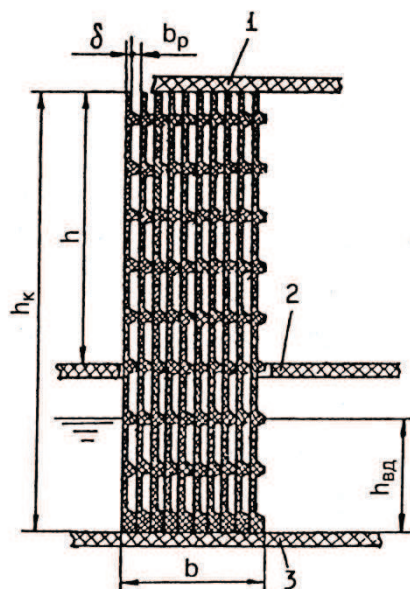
Принципиальная схема устройства и компоновки орошаемой ламинарной насадки из пластин мипласта для воздухоохладителя: 1 – крышка корпуса; 2 – перегородка поддона; 3 – днище поддона; δ – толщина стенки пластины; b_p – ширина воздушного канала; h – рабочая высота насадки; h_k – конструктивная высота насадки; b – ширина пакета насадки; $h_{вд}$ – уровень воды в поддоне
